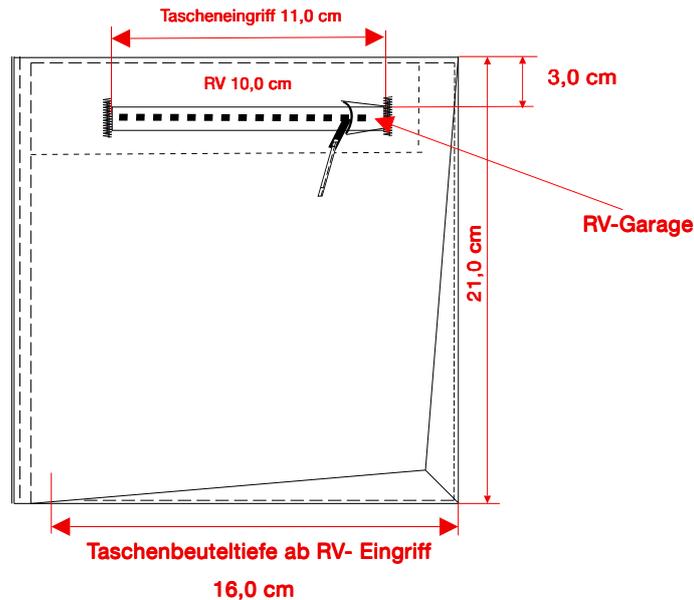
XXXXXXXXXXXXX, Brusttasche Innenansicht
